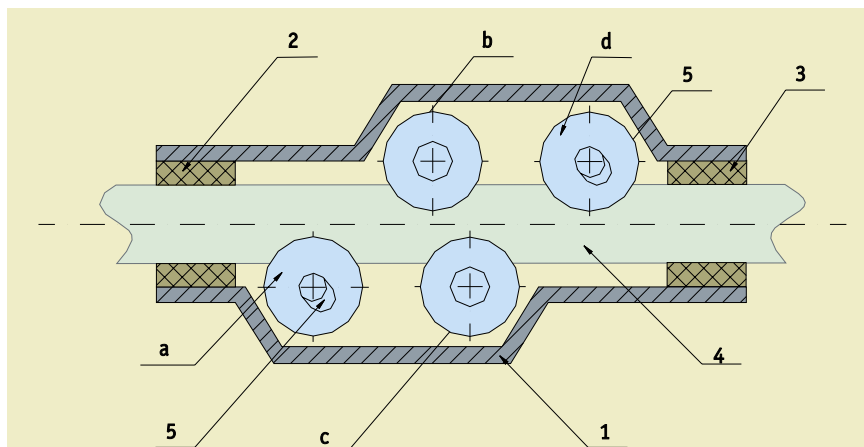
Схема камеры высокого давления, оснащенной гибочными роликами:
